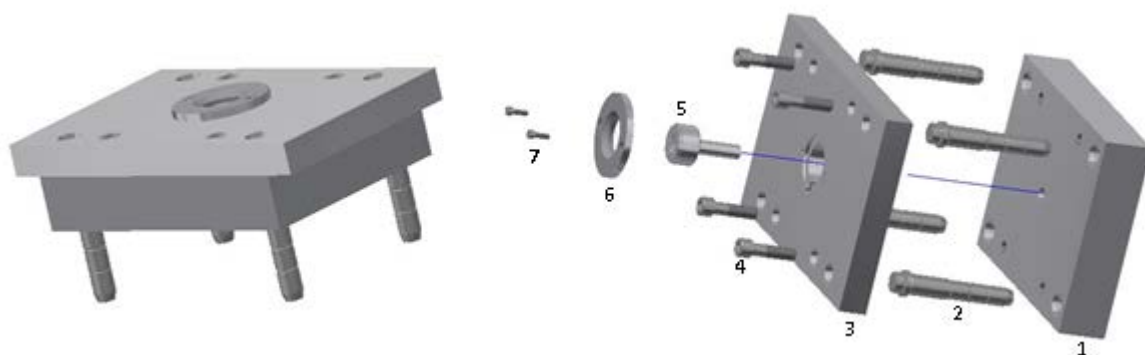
Parte fija del molde de inyección. 1- Placa de las cavidades, 2- Columnas guías, 3- Placa superior, 4- Tornillos M12 x 45, 5- Boquilla, 6- Anillo centrador, 7- Tornillos M5 x 16.
